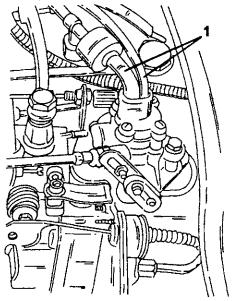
Отсоединить два вакуумных шланга (1) с верхней стороны топливного насоса высокого давления.
